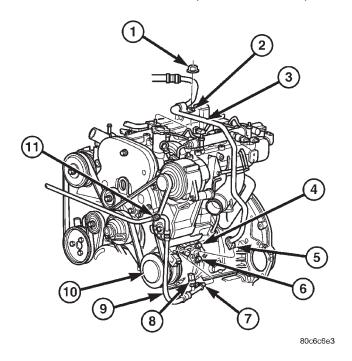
COMPRESOR DE A/A - MOTOR 2.5L DIESEL
